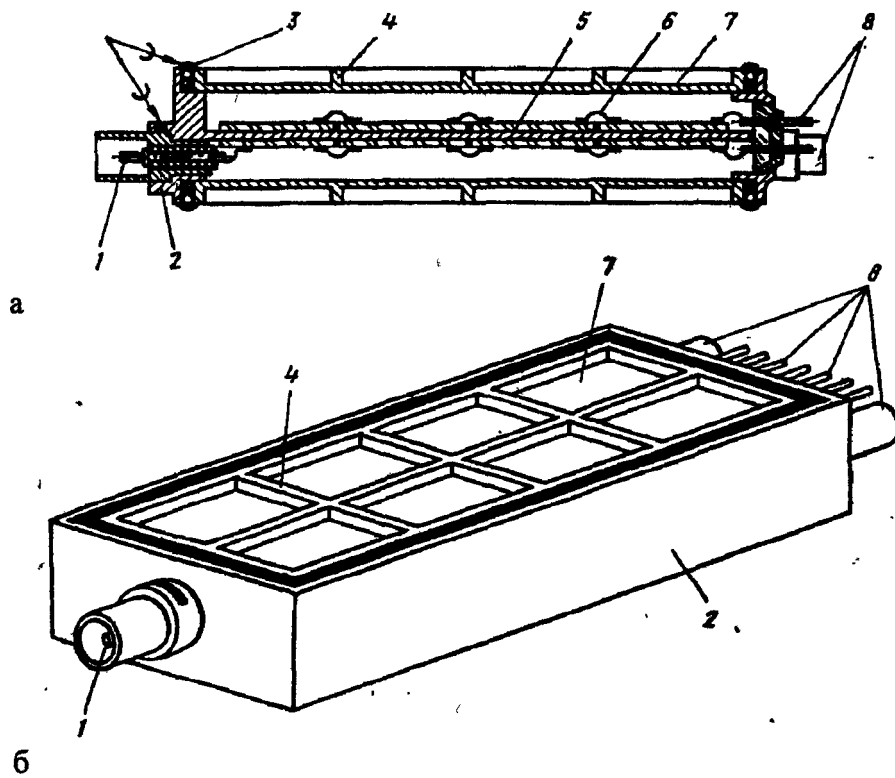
Конструкция модуля СВЧ: а — разрез конструкции; б — изометрия конструкции; 1 — высокочастотный разъем; 2 — каркас-основание; 3 — паяный шов; 4 — ребро крышки; 5 — планка каркаса; 6 — соединительная перемычка; 7 — крышка; 8 — комбинированный разъем
